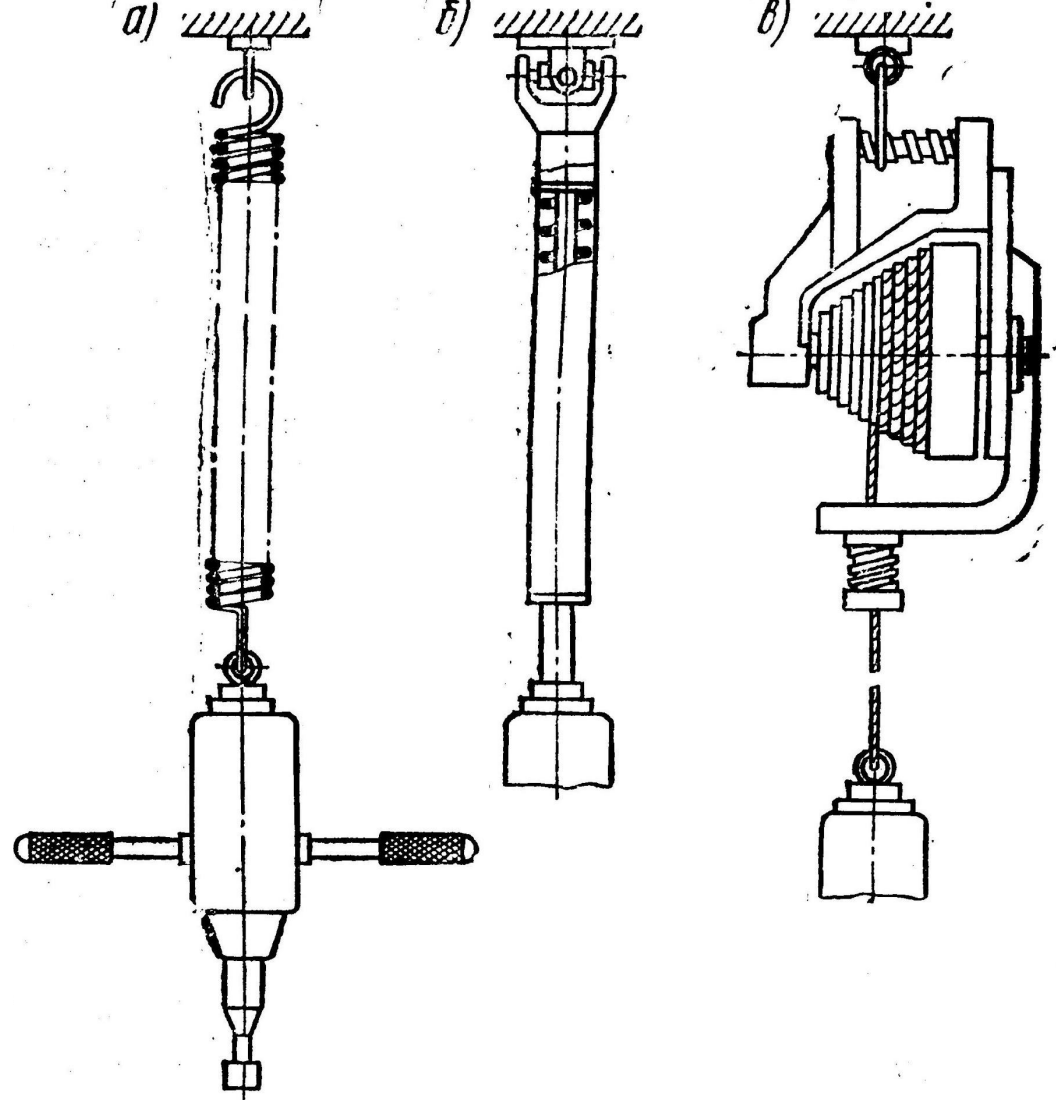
Способы подвешивания механизированного инструмента на эластичных подвесках:
